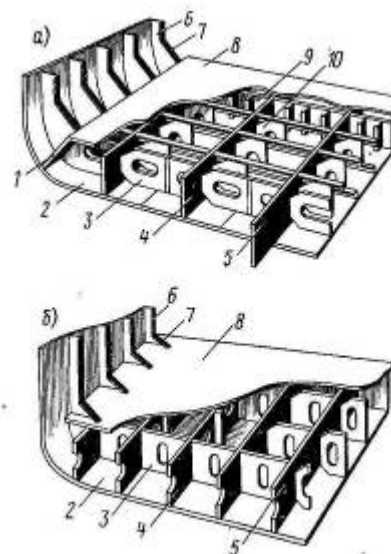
Двойное дно: а — двойное дно со сплошными и бракетными флорами; б — двойное дно с днищевыми стрингерами. 1 — крайний междудонный лист; 2 — обшивка днища; 3 — сплошной флор; 4 — днищевый стрингер; 5 — вертикальный киль; 6—шпангоут; 7— скуловая кница; 8 — настил двойного дна; 9 — водонепроницаемый флор; 10— бракетки.
